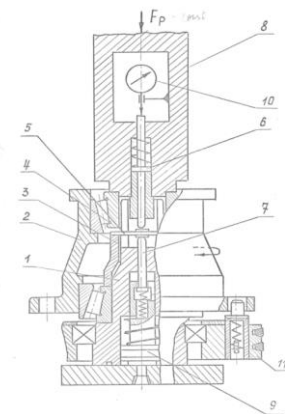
Конструктивная схема установки для измерения требуемой толщины компенсаторного звена для регулирования преднатяга подшипников (1-фальш-оправка, 2-корпус, 3-дистанционная втулка, 4-конический роликоподшипник, 5-измерительный щуп, 6-верхний шток, 7-нижний шток, 8-пиноль для нагружения дуплекса подшипников измерительной технологической силой, 9 – поршень пневмоцилиндра для перемещения нижнего и верхнего штоков, 10 – контрольный прибор, 11- привод вращения корпуса)
